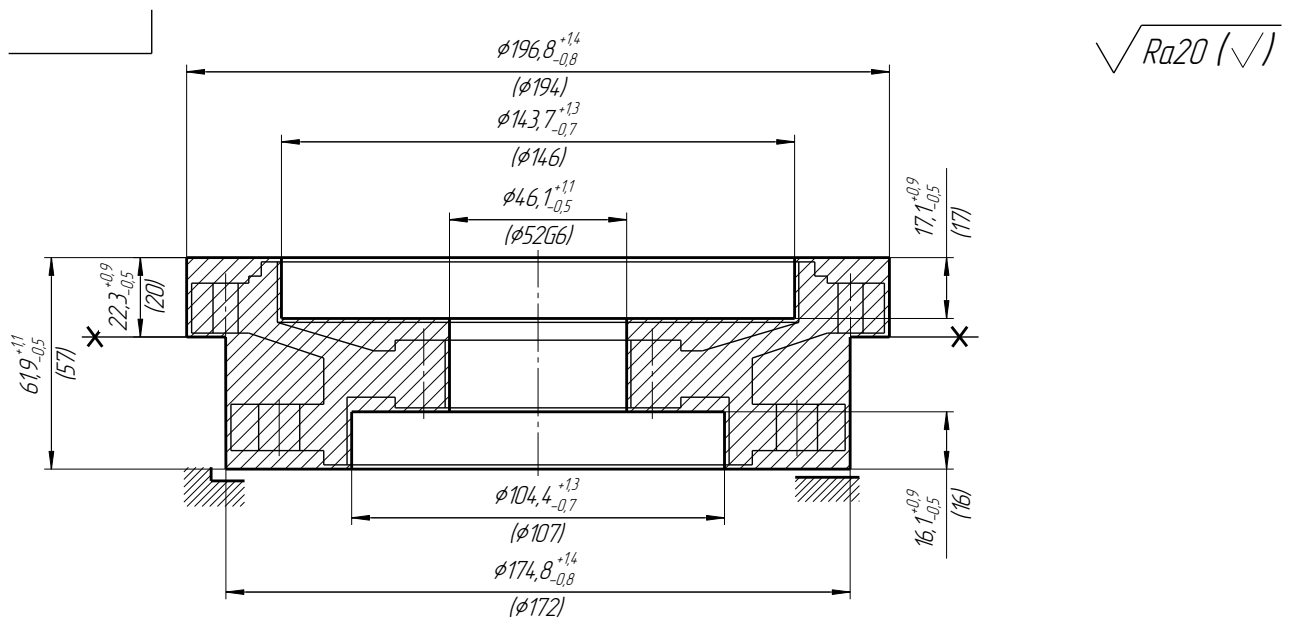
Ескіз заготовки деталі «кришка електродвигуна»
